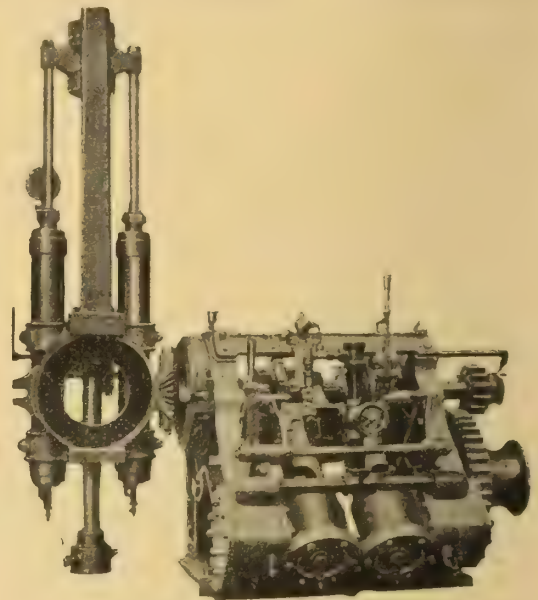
Schürfbohrmaschine mit mehrzylindrigem Druckluft- oder Dampfmotor. American Diamond Drill Co.
